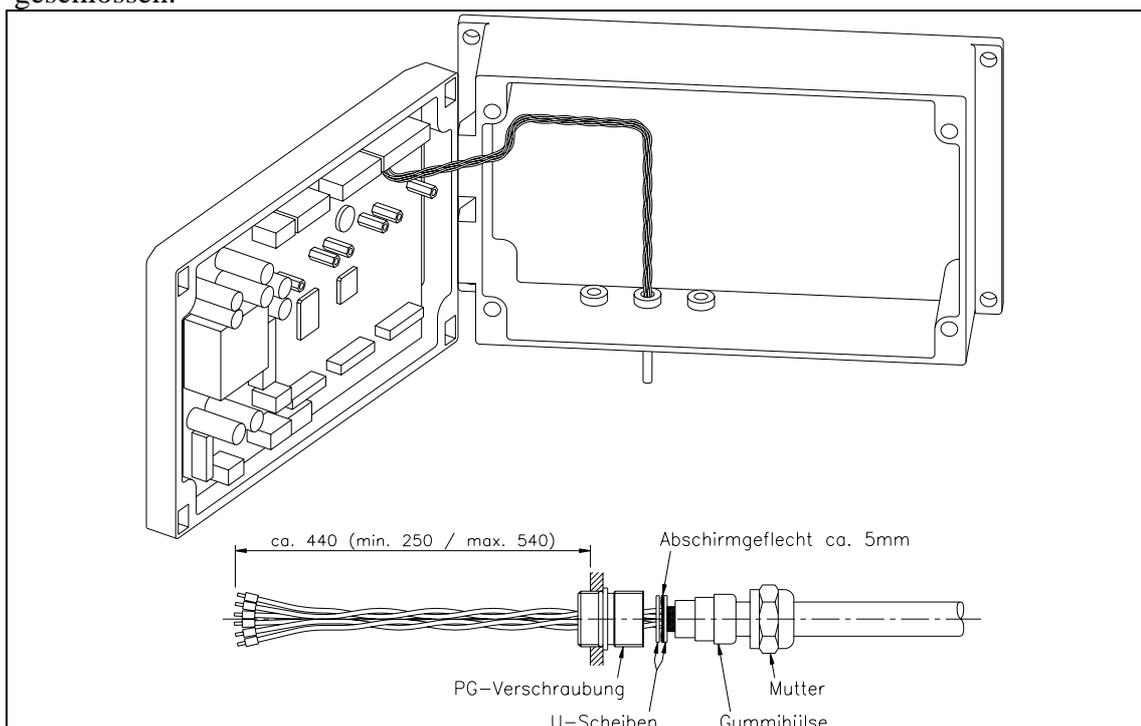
Verlauf der Anschlusskabel im Gehäuse
